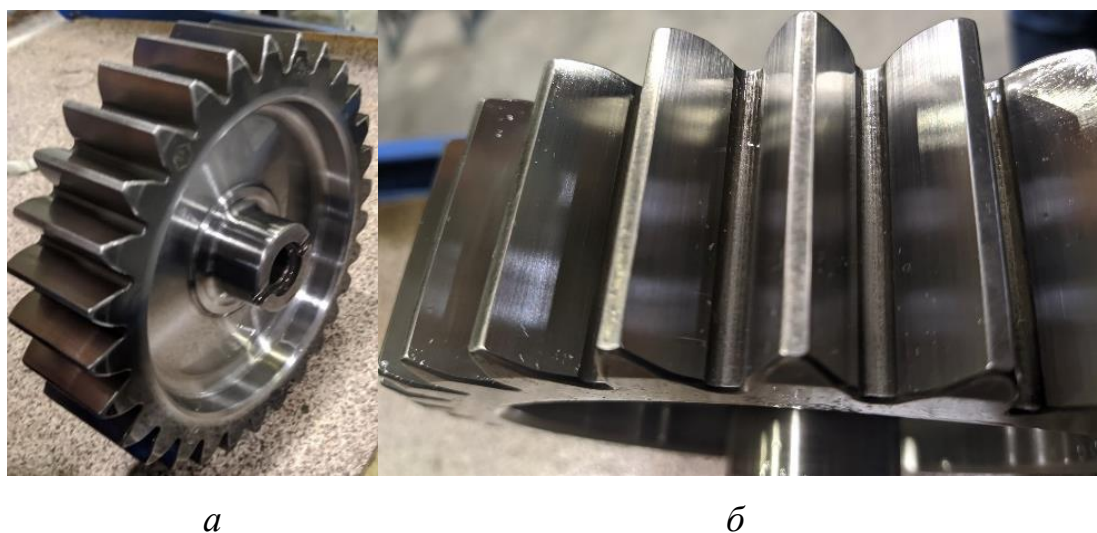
Цилиндрическое зубчатое колесо: *а* – общий вид; *б* – вид сверху
